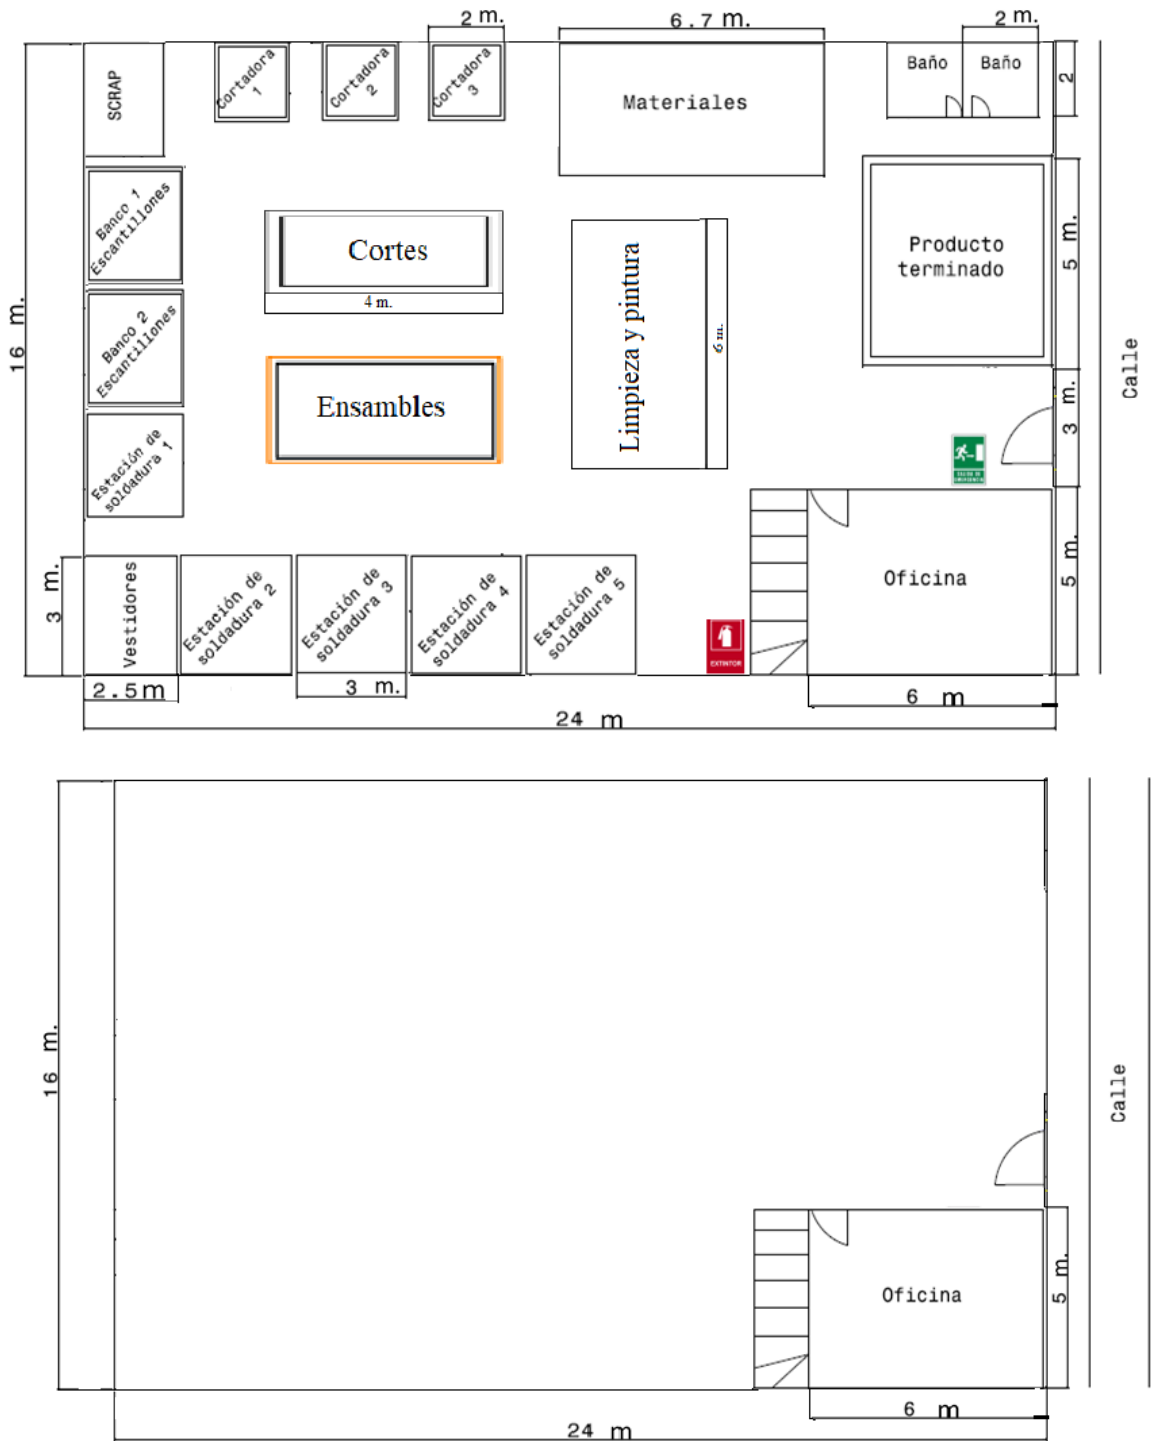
Primera propuesta de *Layout* planta baja y alta
